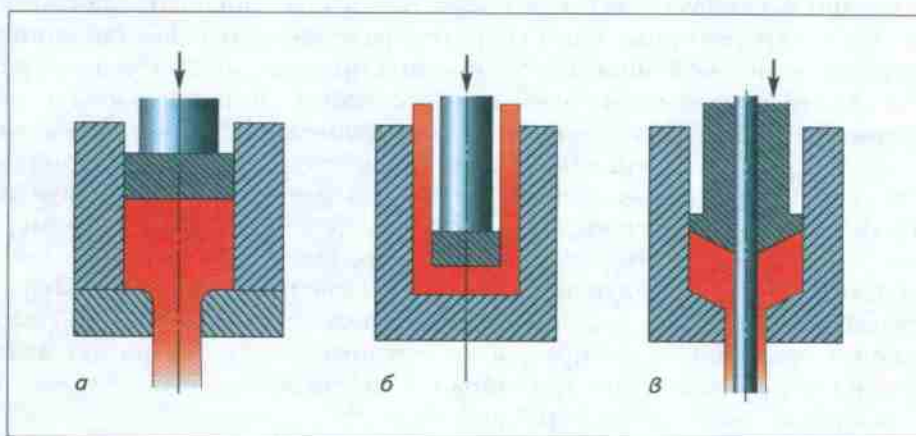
Схемы прессования: а — прямого; б — обратного; в — прессования труб
